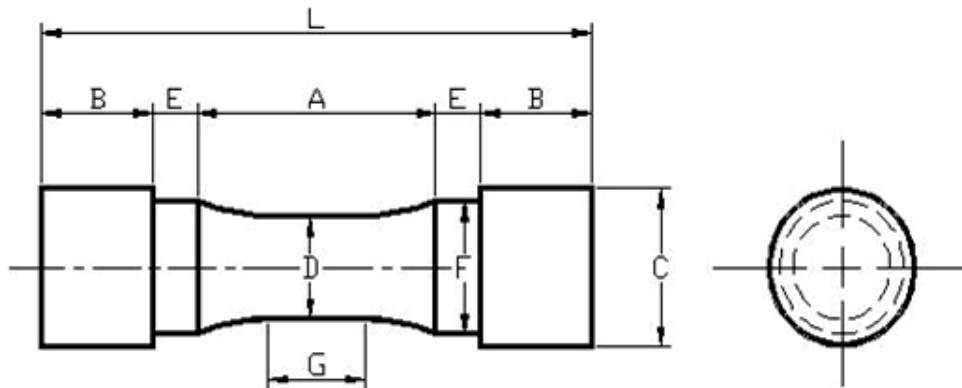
Esquema de la probeta para ensayos de tracción. Las dimensiones indicadas son: A = 32 mm; B = 25 mm; C = 20 mm; D = 12,5 mm; E = 6 mm; F = 16 mm; G = 12,5 mm; L = 95 mm y R = 25 mm.
